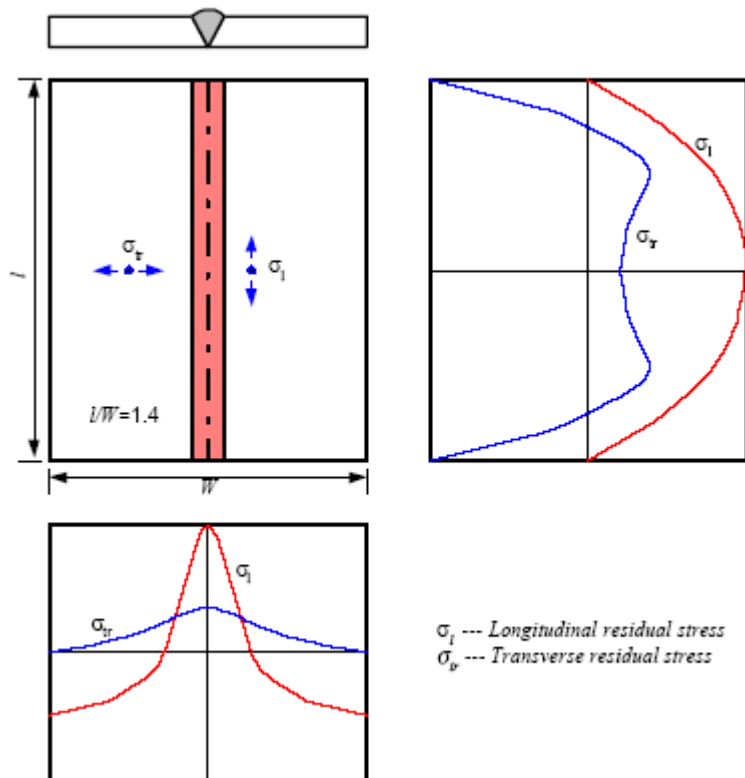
Plancha rectangular con soldadura centrada y tensiones residuales calculadas a lo largo del centro de su sección.
